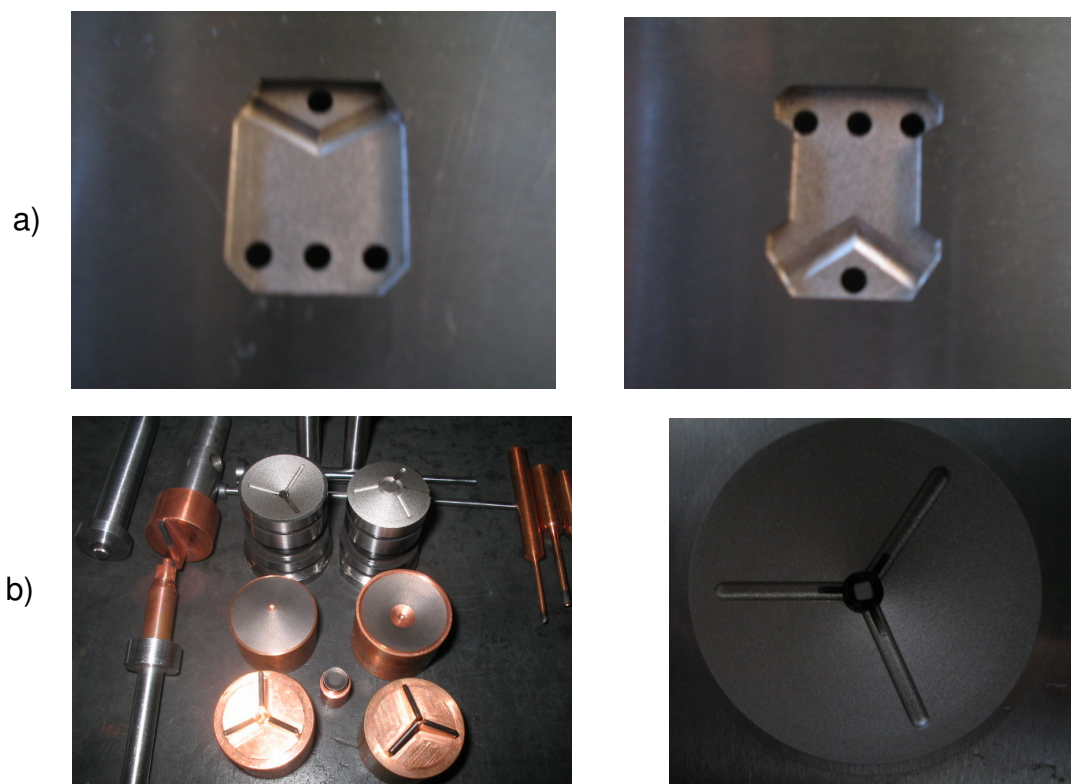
Imagens obtidas durante a confecção das cavidades: a) molde dos grupamentos aminas e carboxila; b) molde do carbono-alfa
